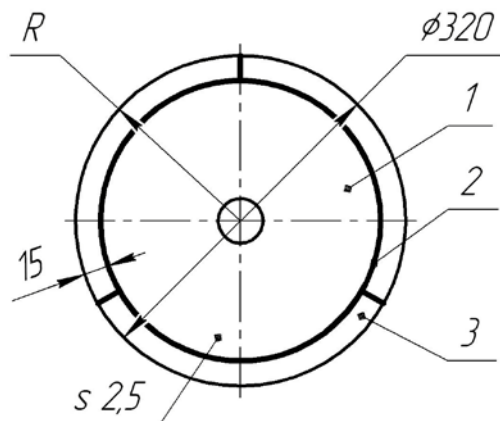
Схема приваривания сегментов к восстанавливаемой поверхности диска: 1 – базовая деталь; 2 – круговой сварной шов; 3 – сегментная шина
